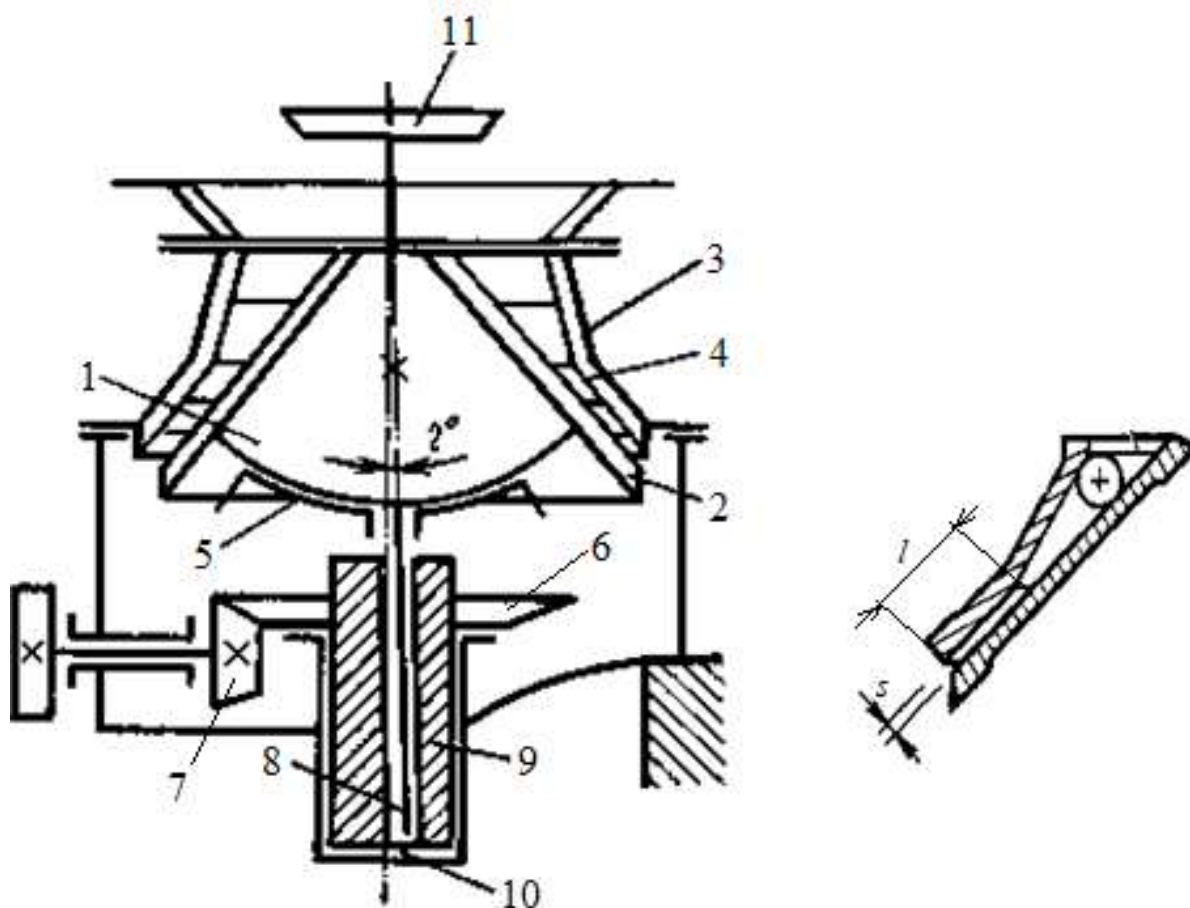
Схема конусної дробарки дрібного дроблення [5-8, 15-18]: 1 – конус рухомий; 2 – футерування конусу рухомого; 3 – конус нерухомий; 4 – футерування конусу нерухомого; 5 – підшипник сферичний; 6 – колесо зубчасте конічне; 7 – вал приводний з конічною шестернею; 8 – вал конуса; 9 – стакан ексцентриковий; 10 – підп’ятник; 11 - таріль розподільча
